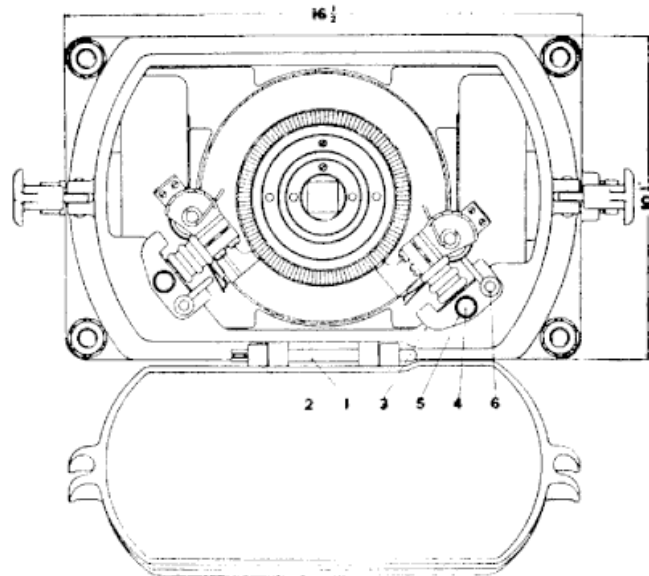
Vue en bout du Moteur et des Porte-Balais.
